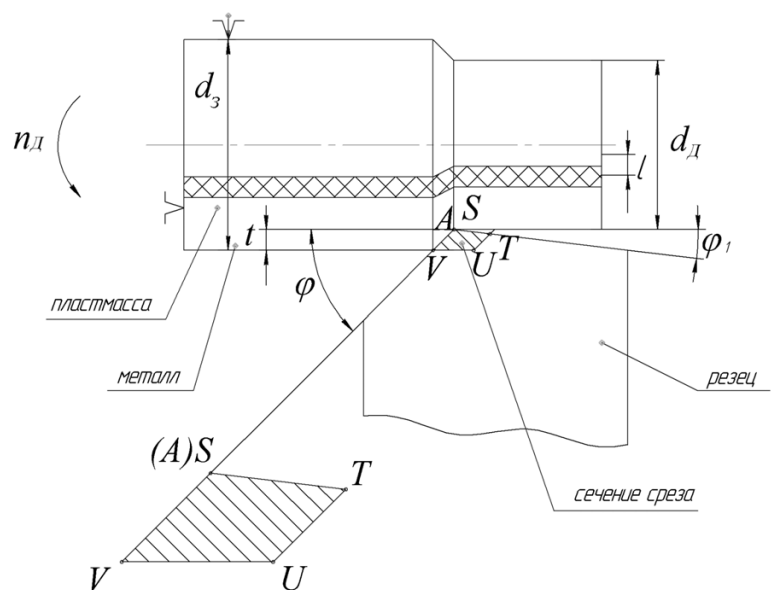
Возможные варианты контакта резец – обрабатываемая поверхность
